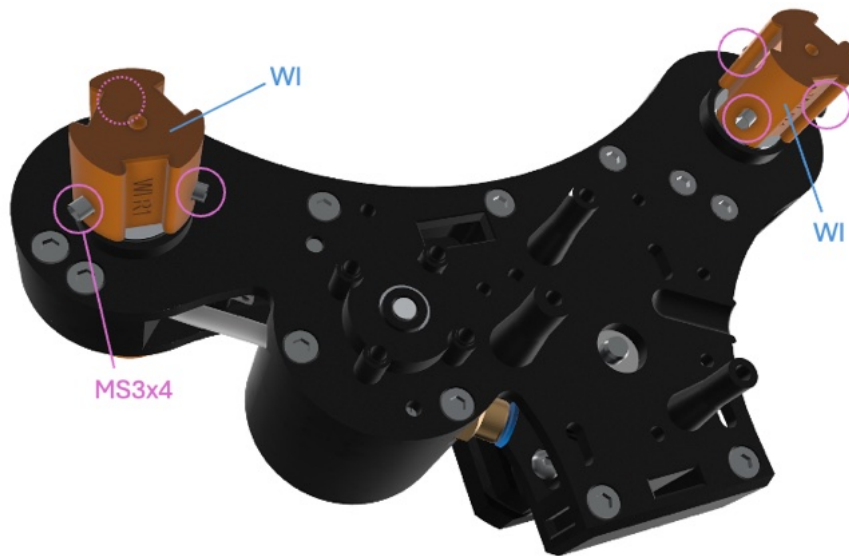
Rewinder-Chassis Montageschritt 24.
